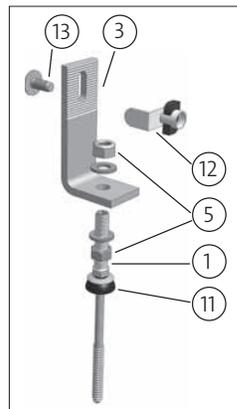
Dispositivo de fijación solar con junta FZD y brida angular
